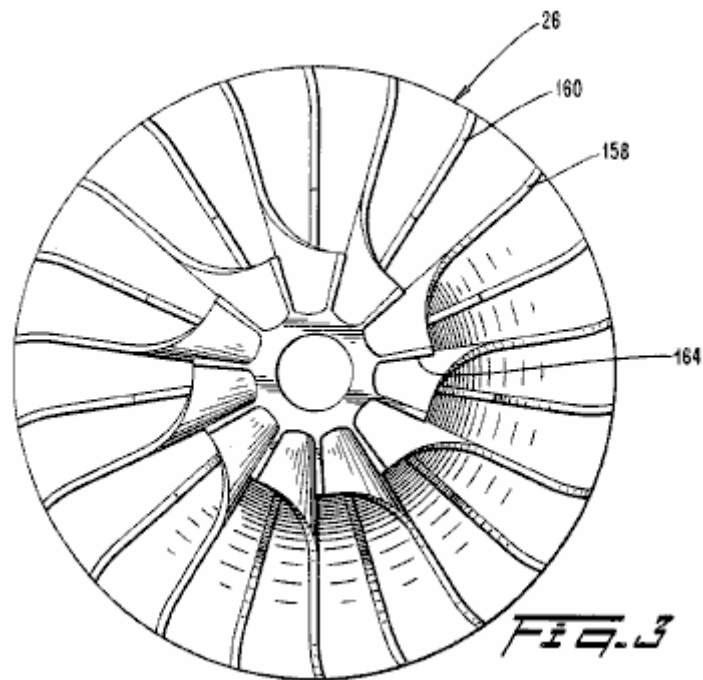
è una vista frontale della girante del compressore di Fig.1;
